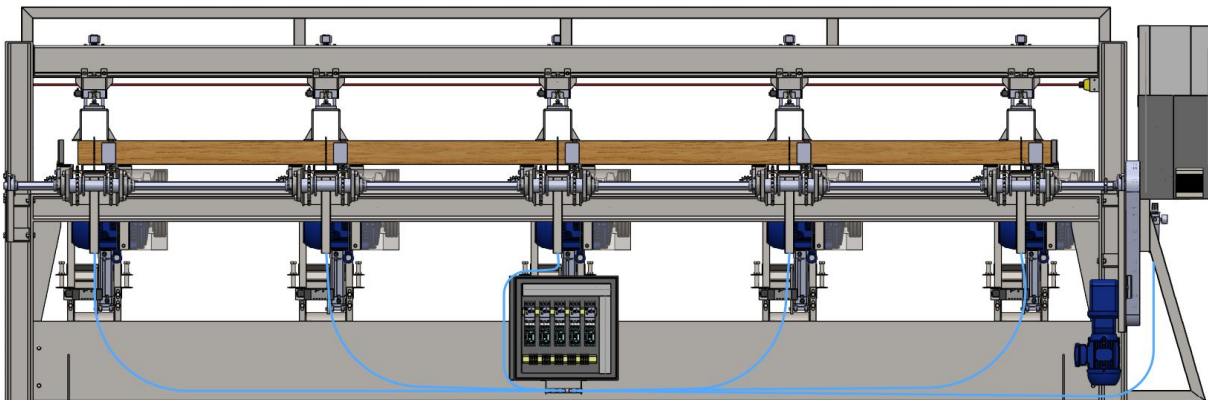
Distribución de mangueras de aire para cada cilindro elevador.
